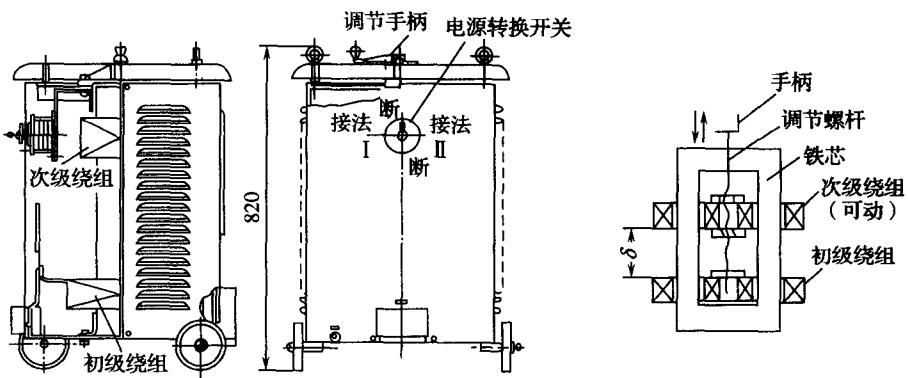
BX3-300 型弧焊变压器及其结构
